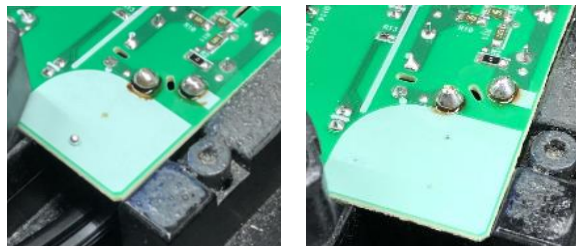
บัดกรีมากเกินไป (Excessive solder)
